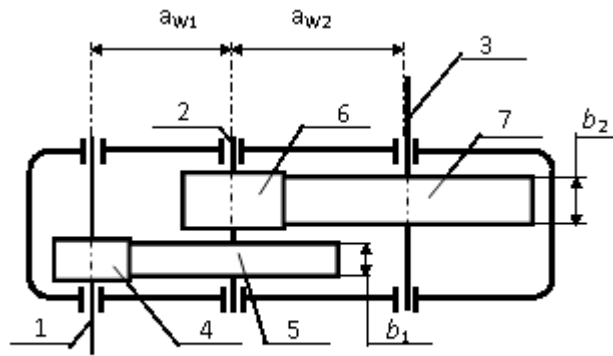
Кинематическая схема двухступенчатого цилиндрического редуктора:
